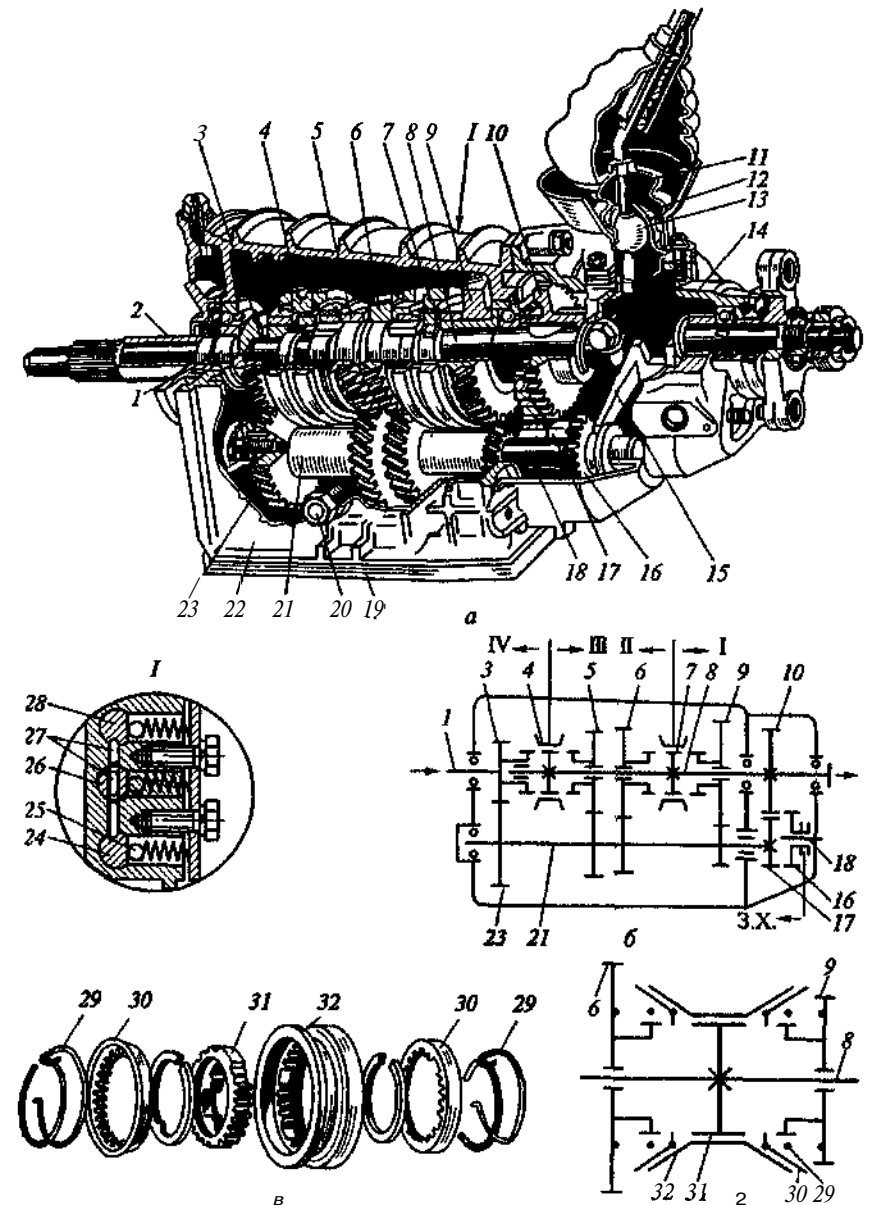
Коробка передач легкового автомобиля ВАЗ:
